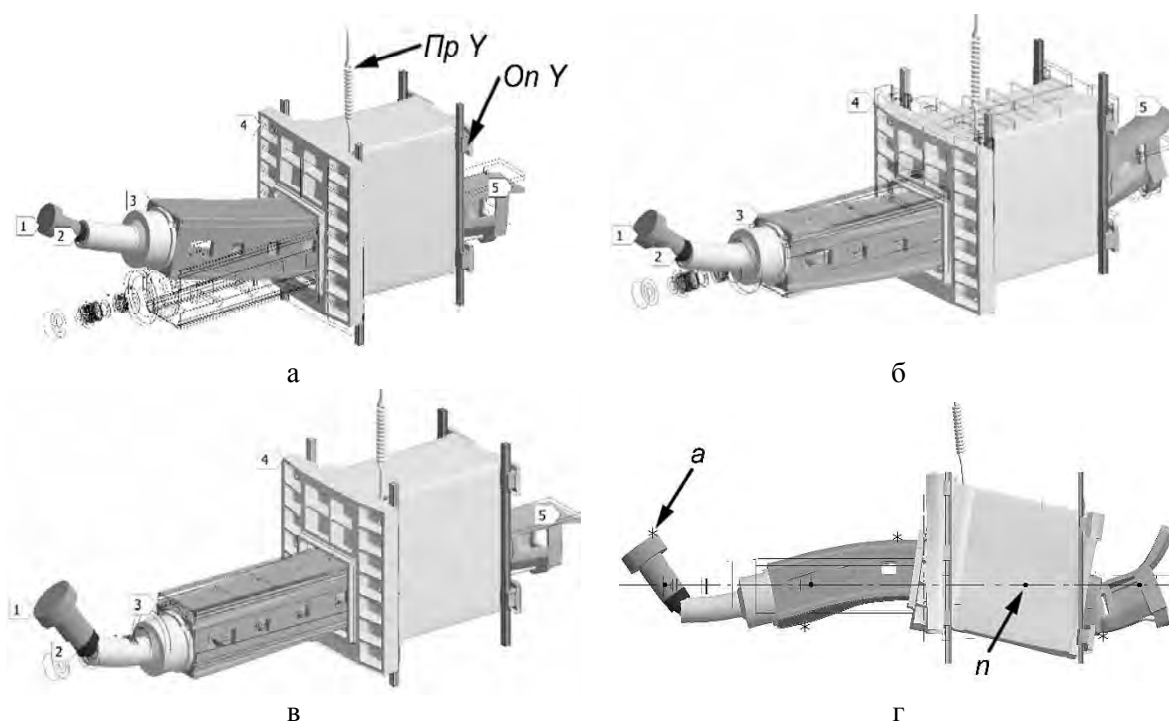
Вертикальные резонансы ползуна 3 (со шпинделем 2 и инструментом 1) в каретке 4 на подвижных направляющих при жесткости пружины-привода : а – клевки (40,34 Гц) ползуна в сборе (1-2-3-5); б – колебания каретки 4 и противофазные махи левого (1, 2, 3) и правого (5 – моторный кронштейн) концов ползуна (80,09 Гц); в – махи инструмента 1 и шпинделя 2 (121,02 Гц) при неподвижности остальных узлов; г – низкоамплитудный многоволновой резонанс ползуна (198,72 Гц) с узлами (n) и пучностями (a)
